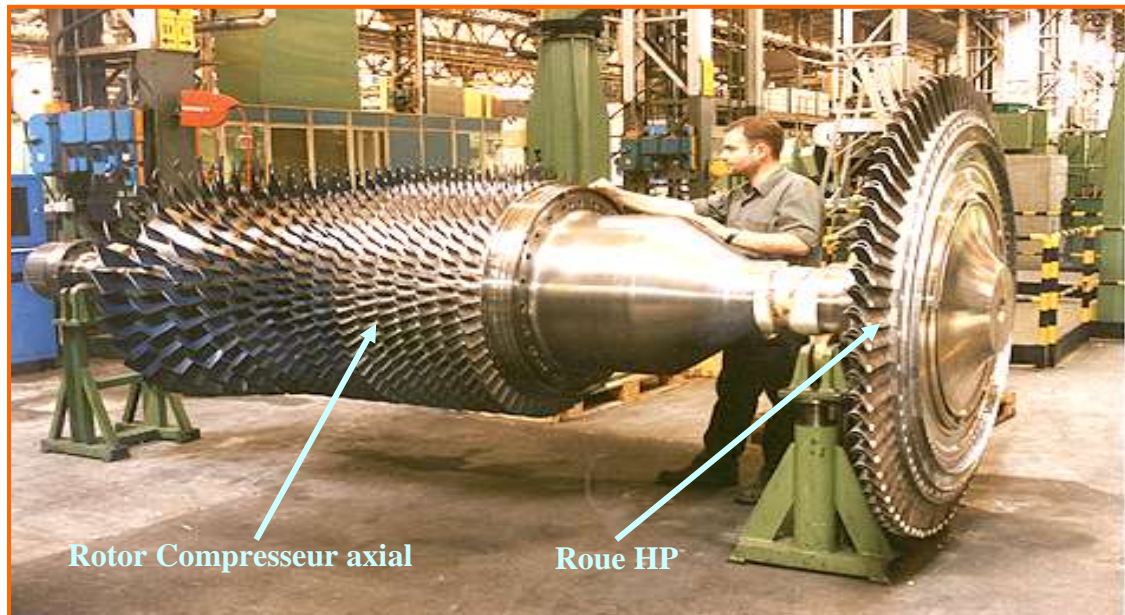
Rotor du Compresseur de la turbine à gaz MS 5002C
